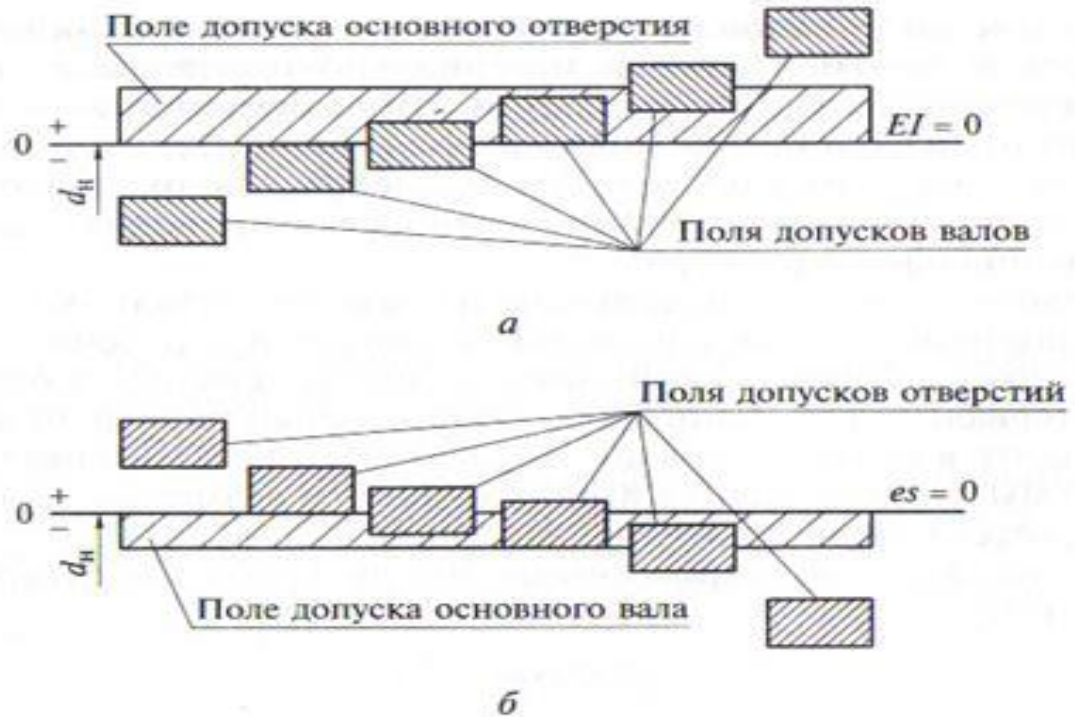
Схема расположения полей допусков вала и отверстия в различных посадках в системах «отверстия» (а) и вала (б)
